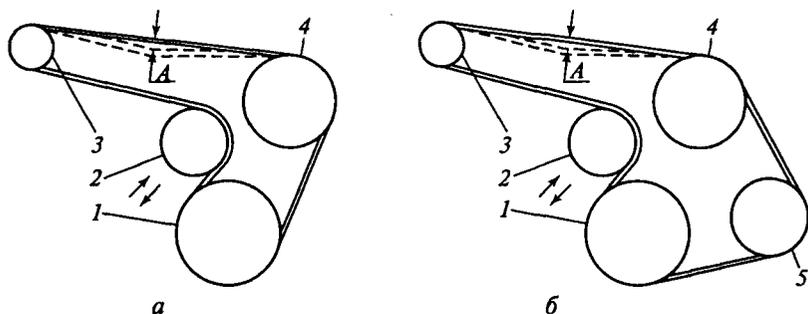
Схема натяжения ремня привода агрегатов:
